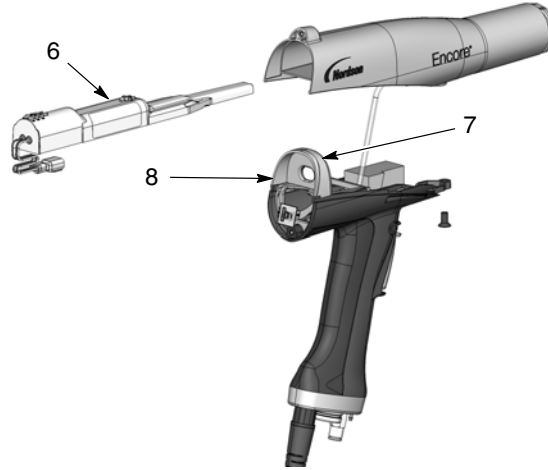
Tabanca Gövdesinin Koldan Ayrılması
